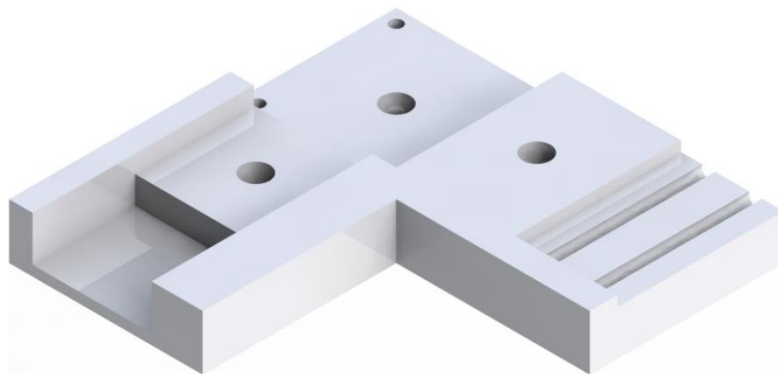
Diseño de pieza CAD mediante SolidWorks®
